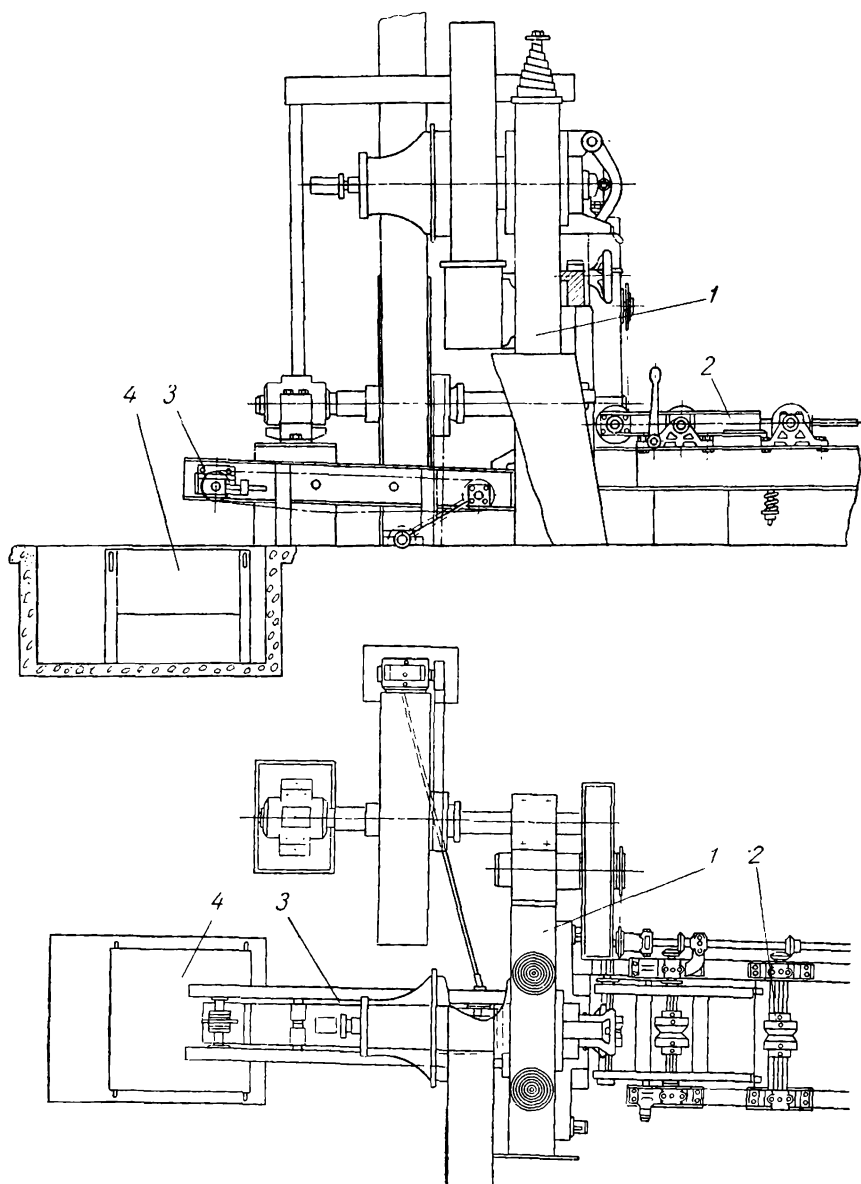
Ножницы с транспортером: 1 — ножницы; 2 — ролик; 3 — транспортер; 4 — тара для заготовок
